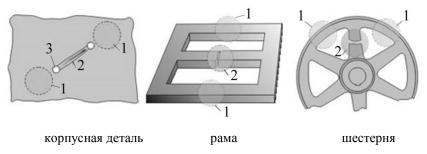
Местный подогрев при сварке деталей из чугуна: I – место подогрева; 2 – место сварки; 3 – отверстия
